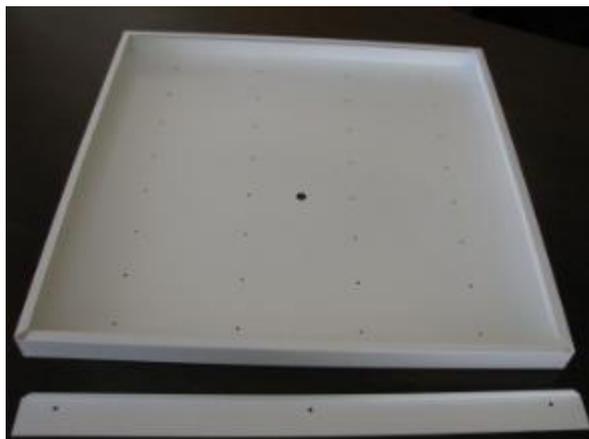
Корпус для светильника типа «Армстронг»
